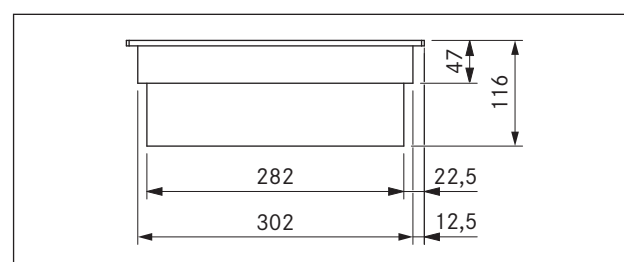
Dimensões do aparelho CKIW, vista frontal
